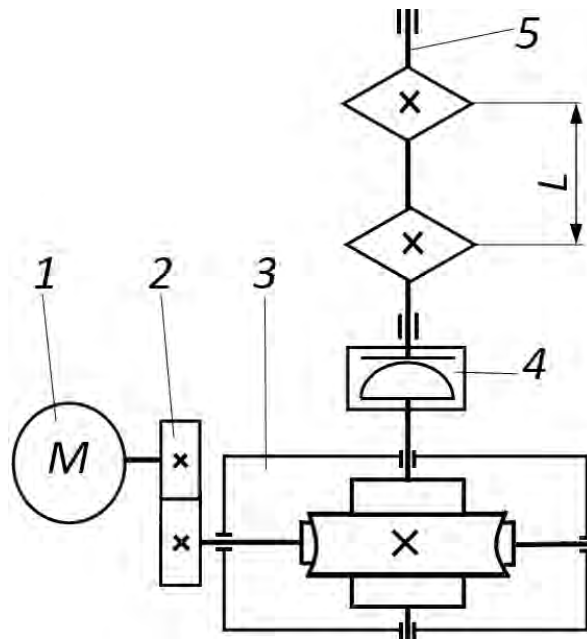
Схема привода цепного конвейера (вид сверху): 1 – асинхронный электродвигатель; 2 – открытая цилиндрическая прямозубая передача; 3 – редуктор червячный с нижним расположением червяка; 4 – муфта зубчатая; 5 – приводной вал с двумя приводными звездочками
